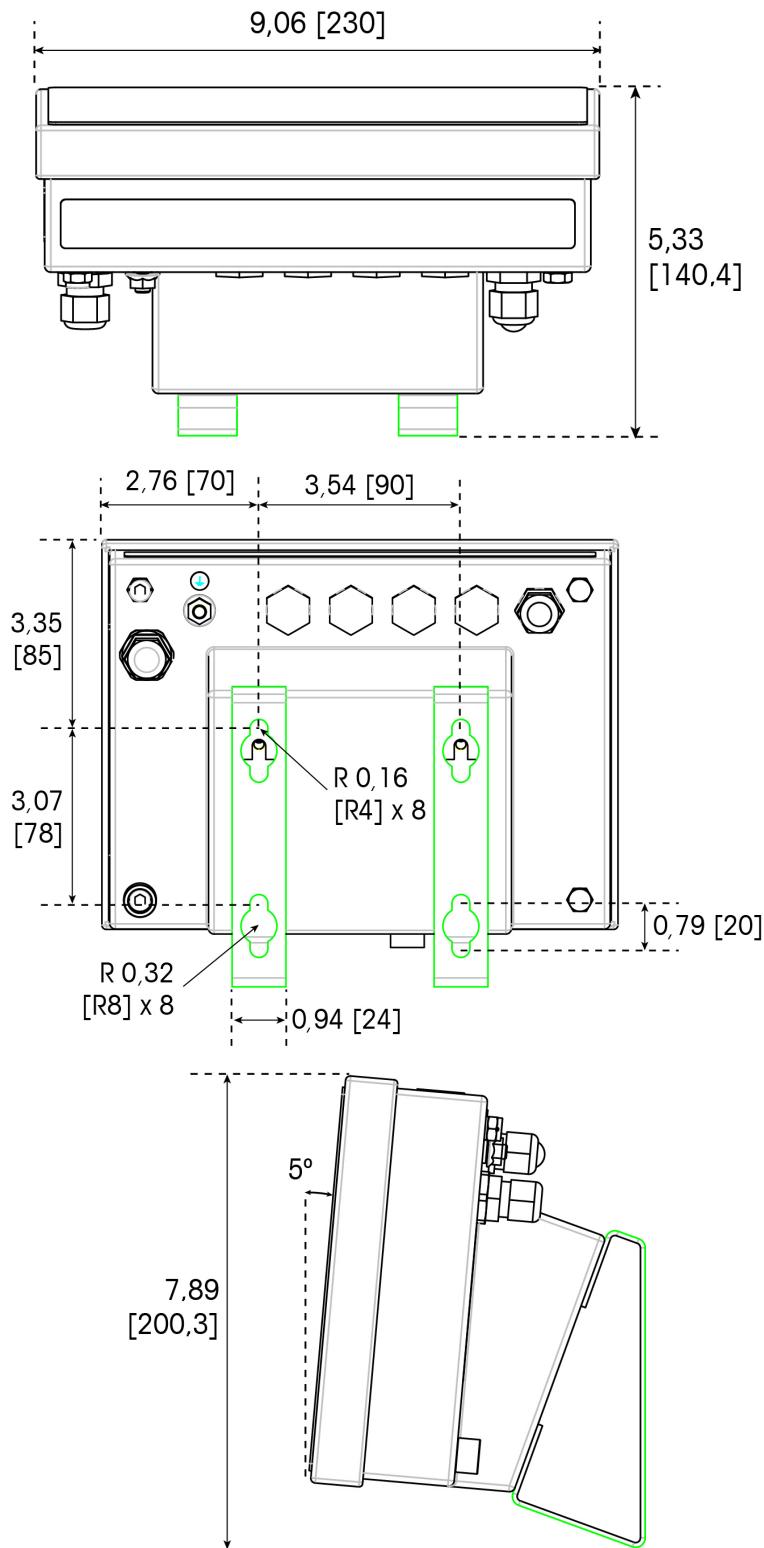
Dimensões IND256x, com suporte fixo de montagem na parede
